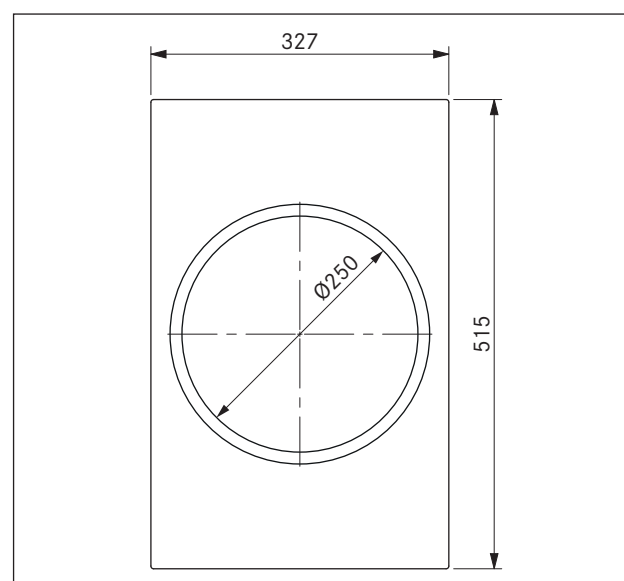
Dimensões do aparelho CKIW, vista de cima
